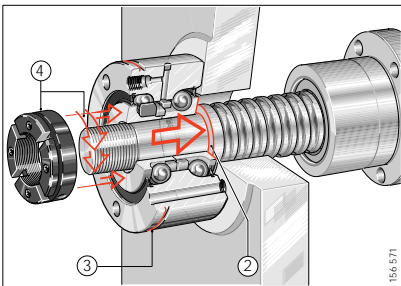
Axial-Schräggugellager ZKLF [5] – Lager auf die Gewindespindel montieren
